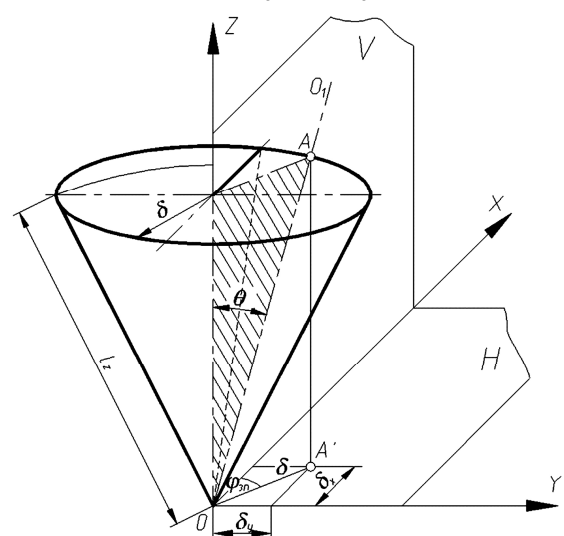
Схема для визначення похибок обробки зубців виробу, зумовлених обертами осей зубчастого колеса та пристрою
